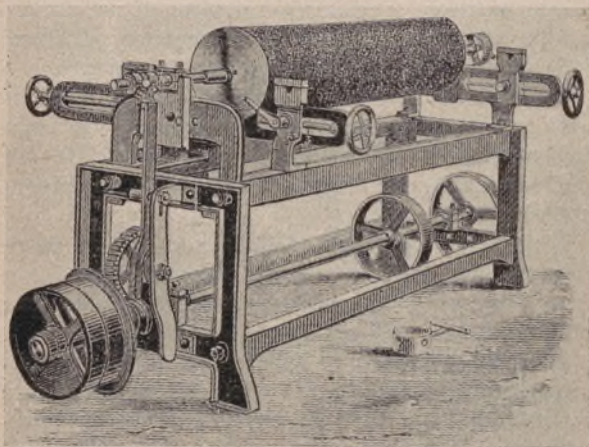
Banco a molare e suo cilindro smerigliatore per cilindri lavoratori, volteggiatori, volante ecc.
